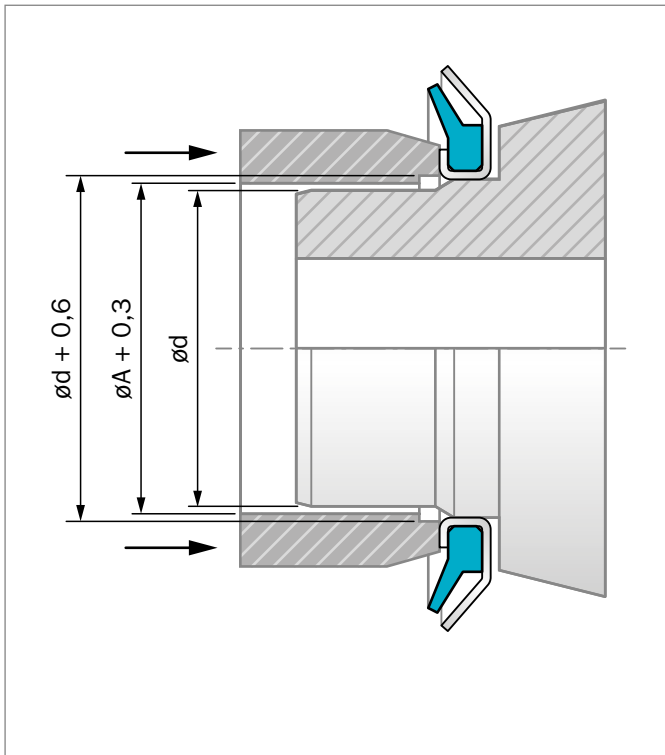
Montagewerkzeug; bei der Montage gegen einen Ansatz darf die Montagekraft nicht zu groß sein, damit das Gehäuse des GAMMA Rings nicht beschädigt wird.
